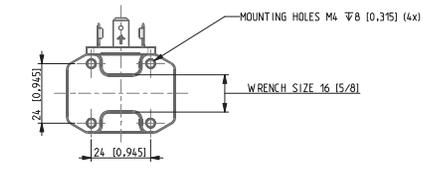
Dimensions 1/4" en ligne, largeur de la bobine
